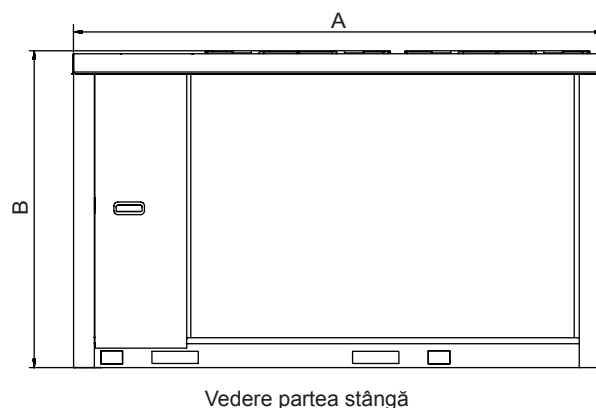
Schiță dimensională KEM-30 DNS3
